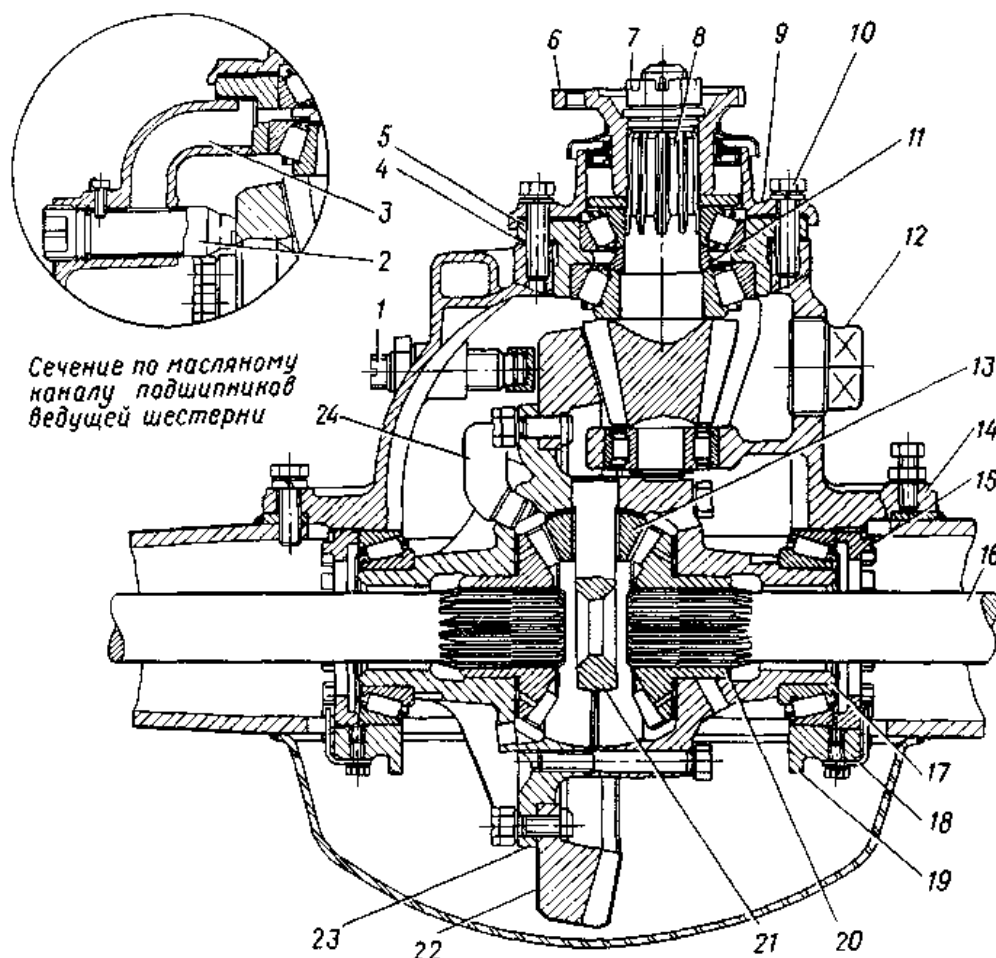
Головна передача: 1 — гвинт упору; 2 — маслоприймочна трубка; 3 — верхній канал; 4 — регулювальні прокладки; 5 — муфта підшипників; 6 — фланець; 7 — гайка; 8 — ведуча шестерня; 9 — кришка; 10 — болт; 11 — регулювальне кільце; 12 — пробка заливного отвору; 13 — сателіт; 14 — картер; 15 — гайка; 16 — піввісь; 17 — права коробка диференціала; 18 — стопорна пластина; 19 — кришка; 20 — напівосьова шестерня; 21 — хрестовина; 22 — ведена шестерня; 23 — ліва коробка диференціала; 24 — маслоуловлювач
